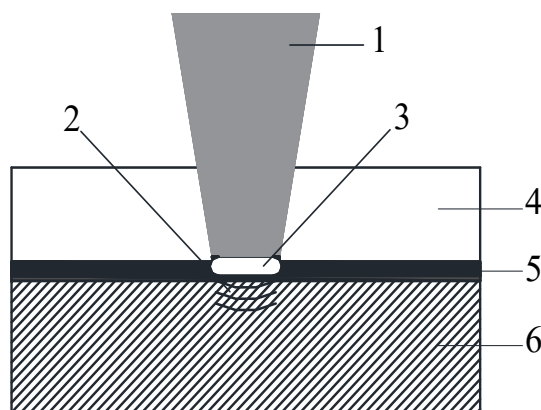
Принципова схема ЛУХ обробки матеріалів: 1 – потік випромінювання, 2 – ударна хвиля; 3 – плазма; 4 – прозоре конденсоване середовище; 5 – абсорбент; 6 – металевий зразок
